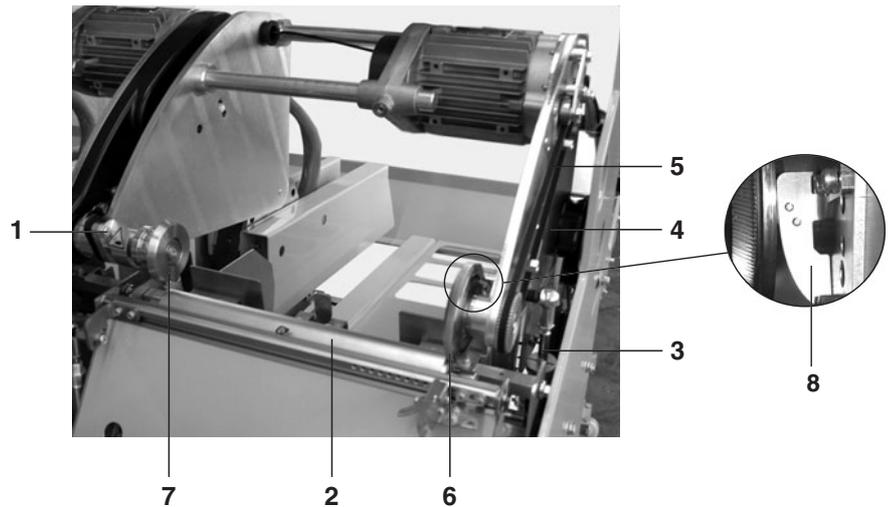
Gruppo di avvolgimento, vista frontale destra
